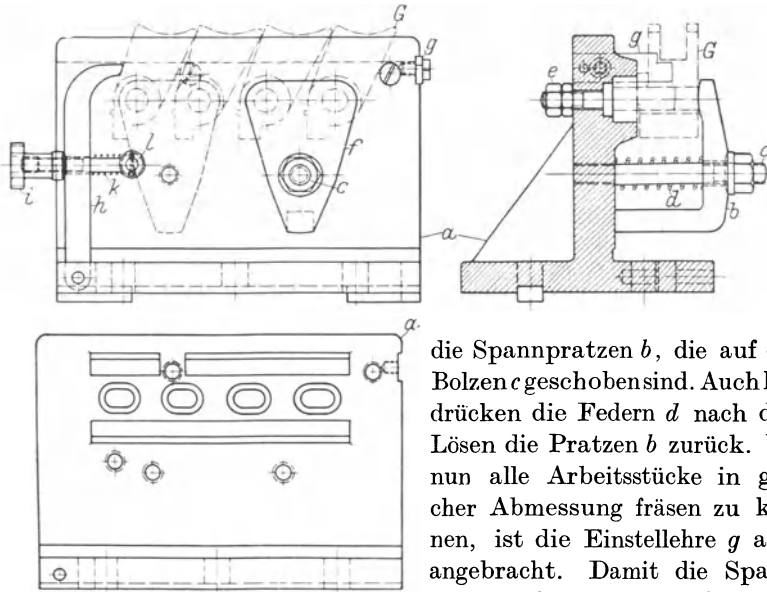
Fräsvorrichtung für Ausrückgabeln.
